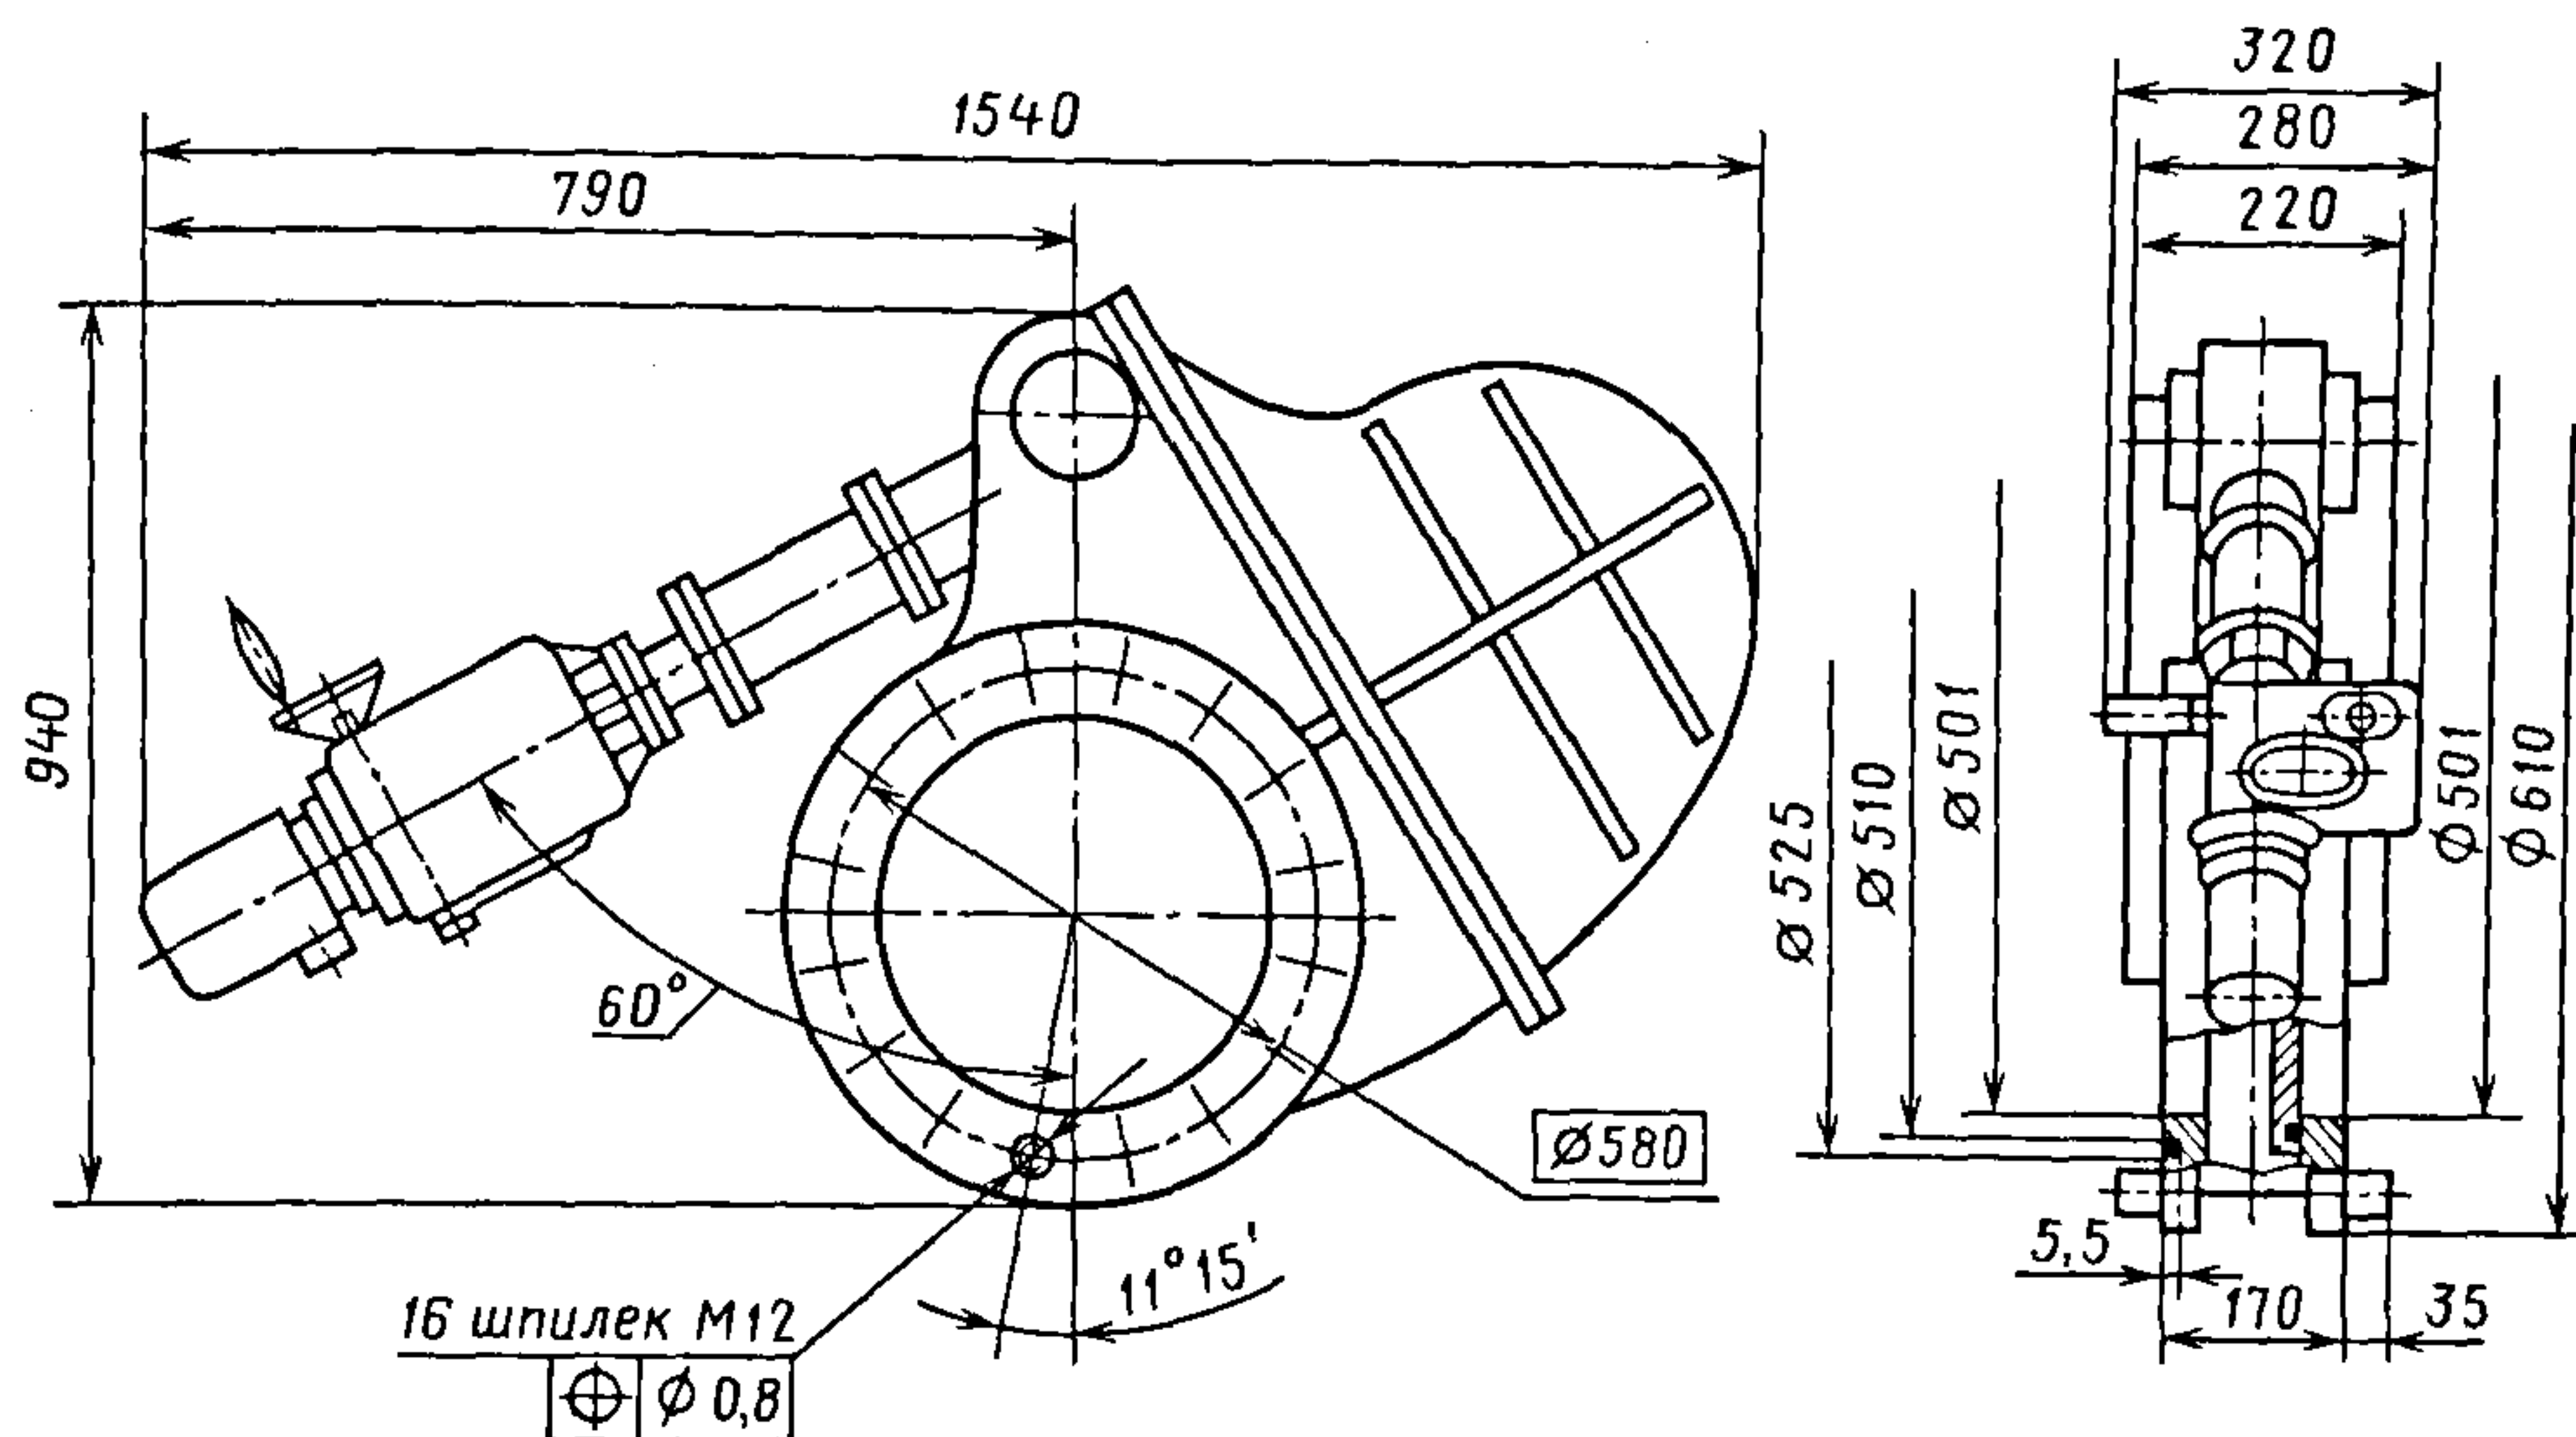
Габаритный чертеж затвора 23ВЭ-500
